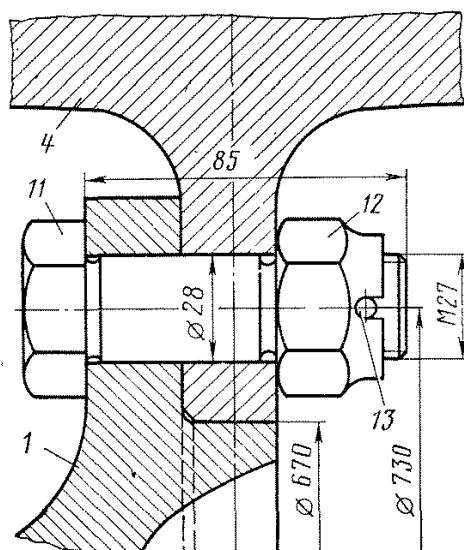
Крепление зубчатого колеса к колесному центру
